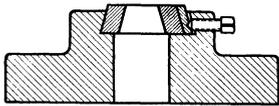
Befestigung der Schnittplatte durch Schwabenschwanz und Druckschraube.
